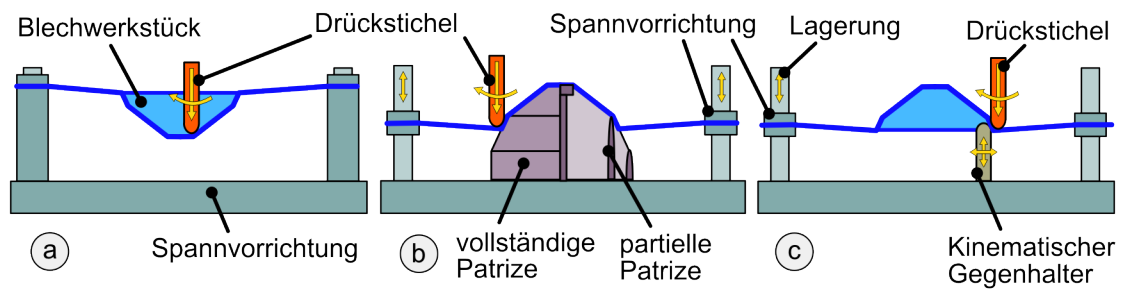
Prozessvarianten in der IBU: a) ohne Gegenwerkzeug (SPIF), b) massives und partielles Gegenwerkzeug (TPIF), c) kinematisches Gegenwerkzeug.
